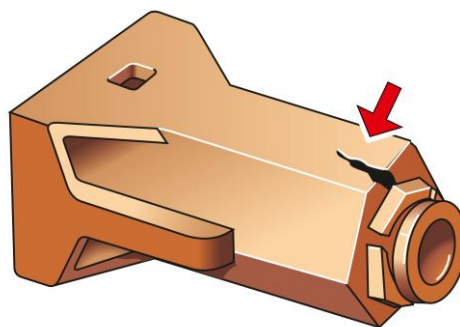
Трещины в корпусе поглощающего аппарата
